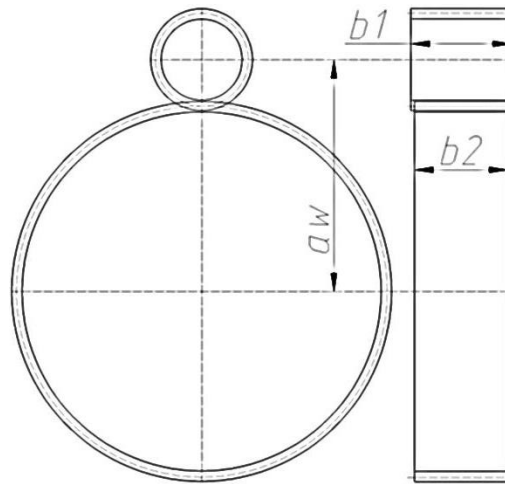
Схема цилиндрической передачи без смещения
